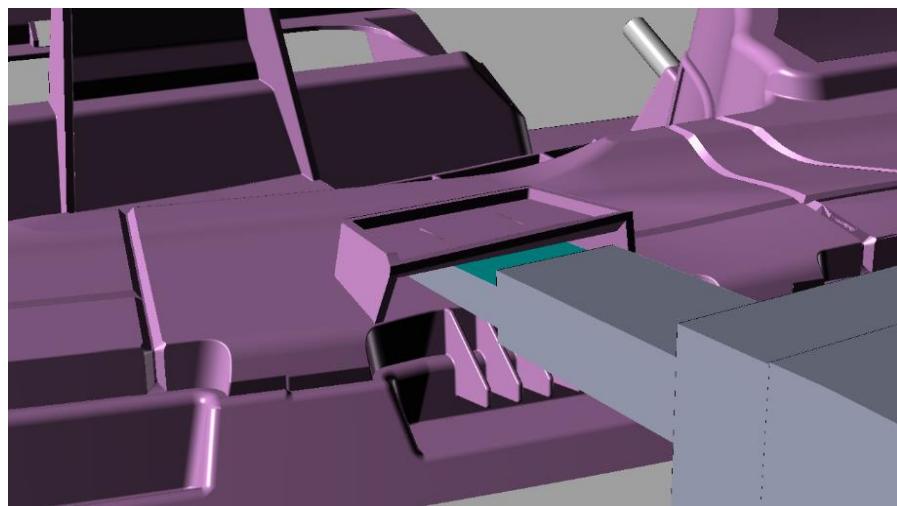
CAD Pieza del posicionador para RPS (Z3-Z4)
